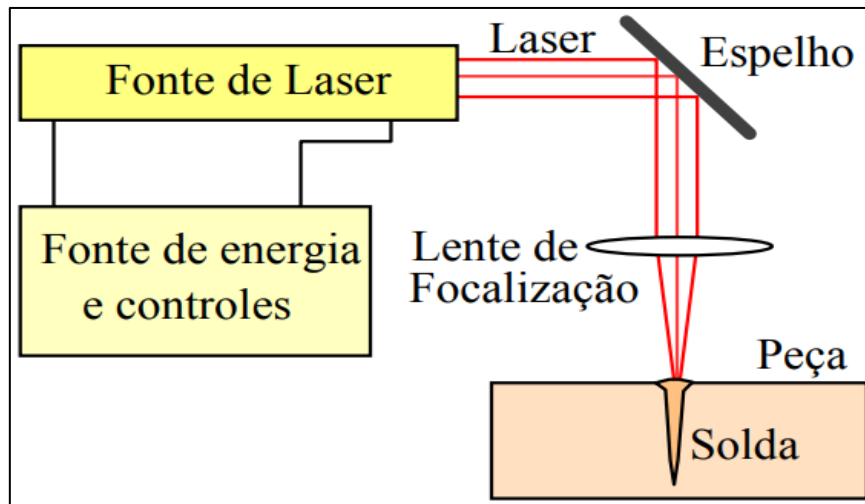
Elementos de um sistema típico para soldagem a laser
